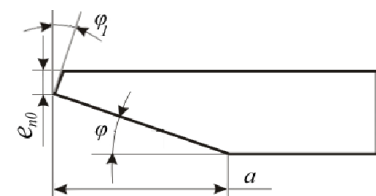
Профіль різця для обробки опуклої сторони зуба
